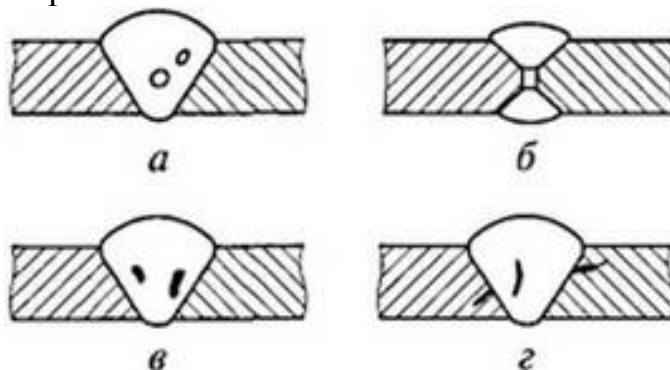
Внутрішні дефекти зварного шва:
